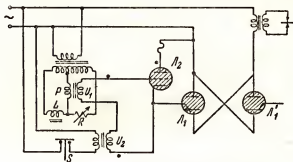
Схема синхронного включения сварочного тока.
